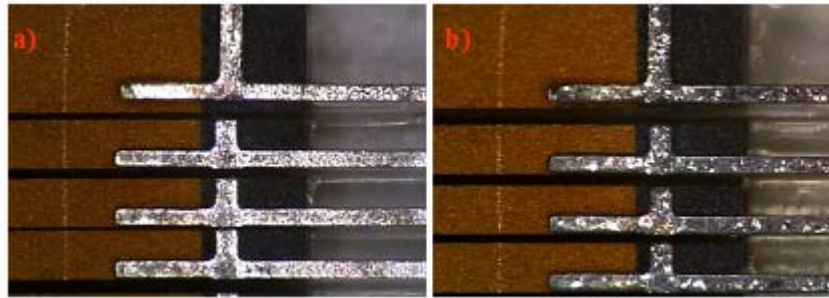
crack della ceramica e della saldatura sugli elementi 1 e 2 della zona a destra dell'array del campione SAC305 dopo le prove termiche.
